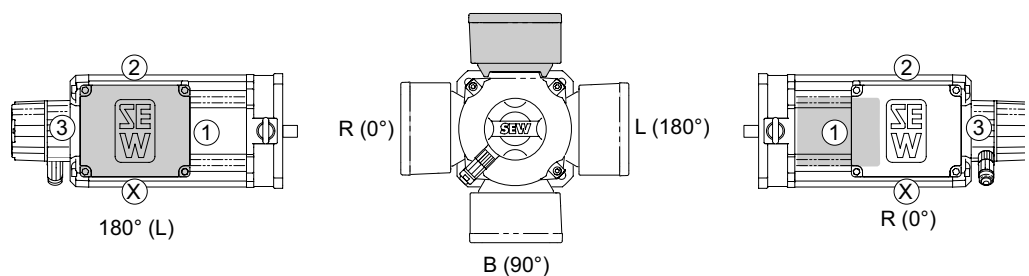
Lage des Klemmenkastens und der Kabeleinführung
